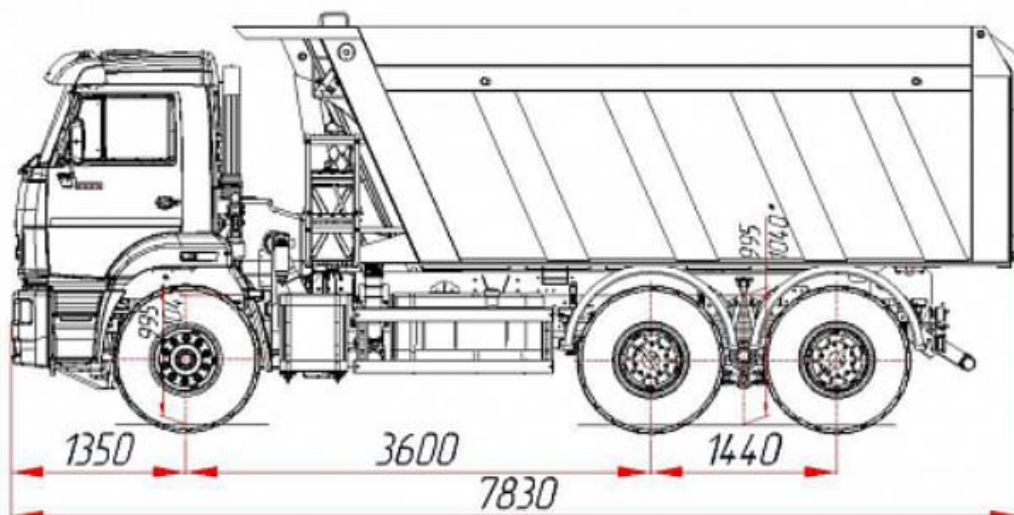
Габаритные размеры самосвала Камаз 6520-53
